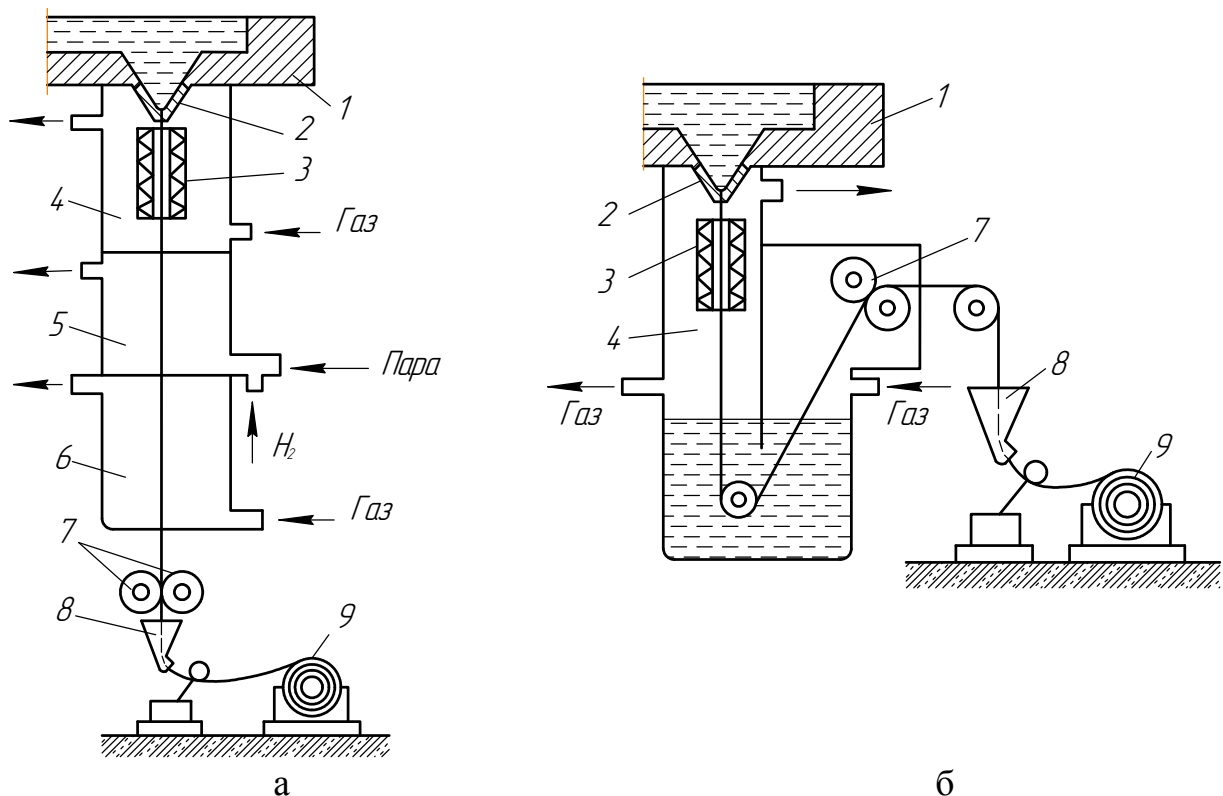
Схеми установок для металізації скловолокон з парової фази (а) та з розплав (б): 1 – піч; 2 – прядильна головка; 3 – нагрівач; 4 – газова камера; 5 – камера з парами металу; 6 – відновлювальна камера; 7 – натяжні ролики; 8 – напрямний пристрій; 9 – приймальний барабан
